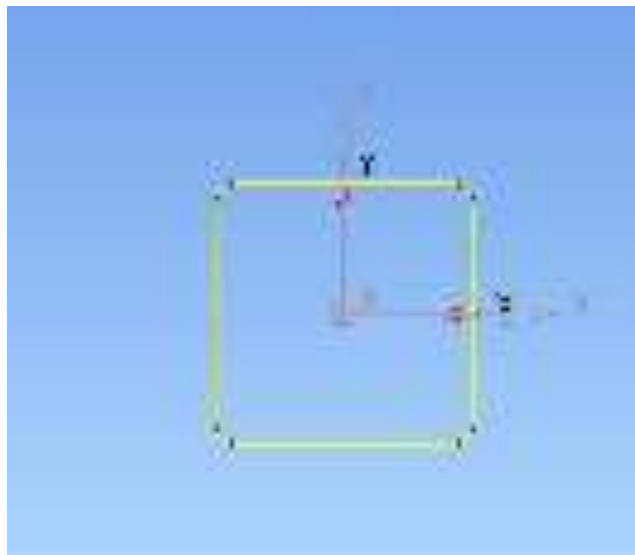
Ескіз нижнього перетину ріжучої пластини (вид зверху)
